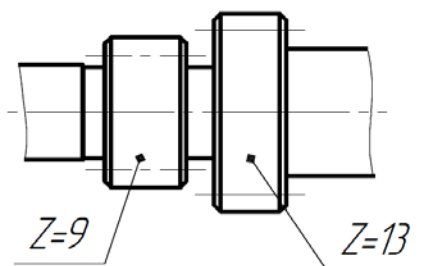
Труднообрабатываемые венцы зубчатых колес
